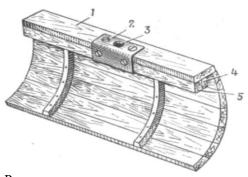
Подуключина: 1 — планширь; 2 — подуключина; 3 — отверстие для уключины; 4 — деревянный заполнитель; 5 — привальный брус
